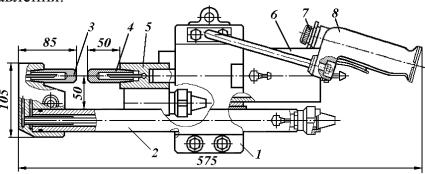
Сварочные клещи КТП-8-2
